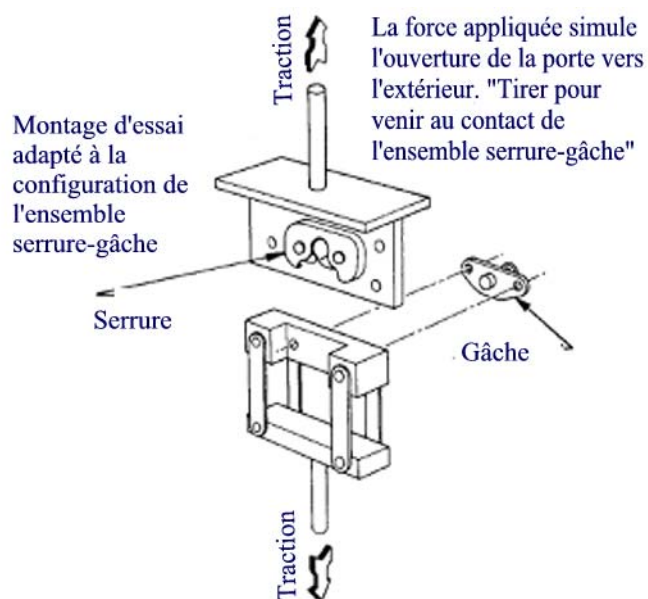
Serrure de porte – Montage pour essai n° 2 d'application d'une force de traction
